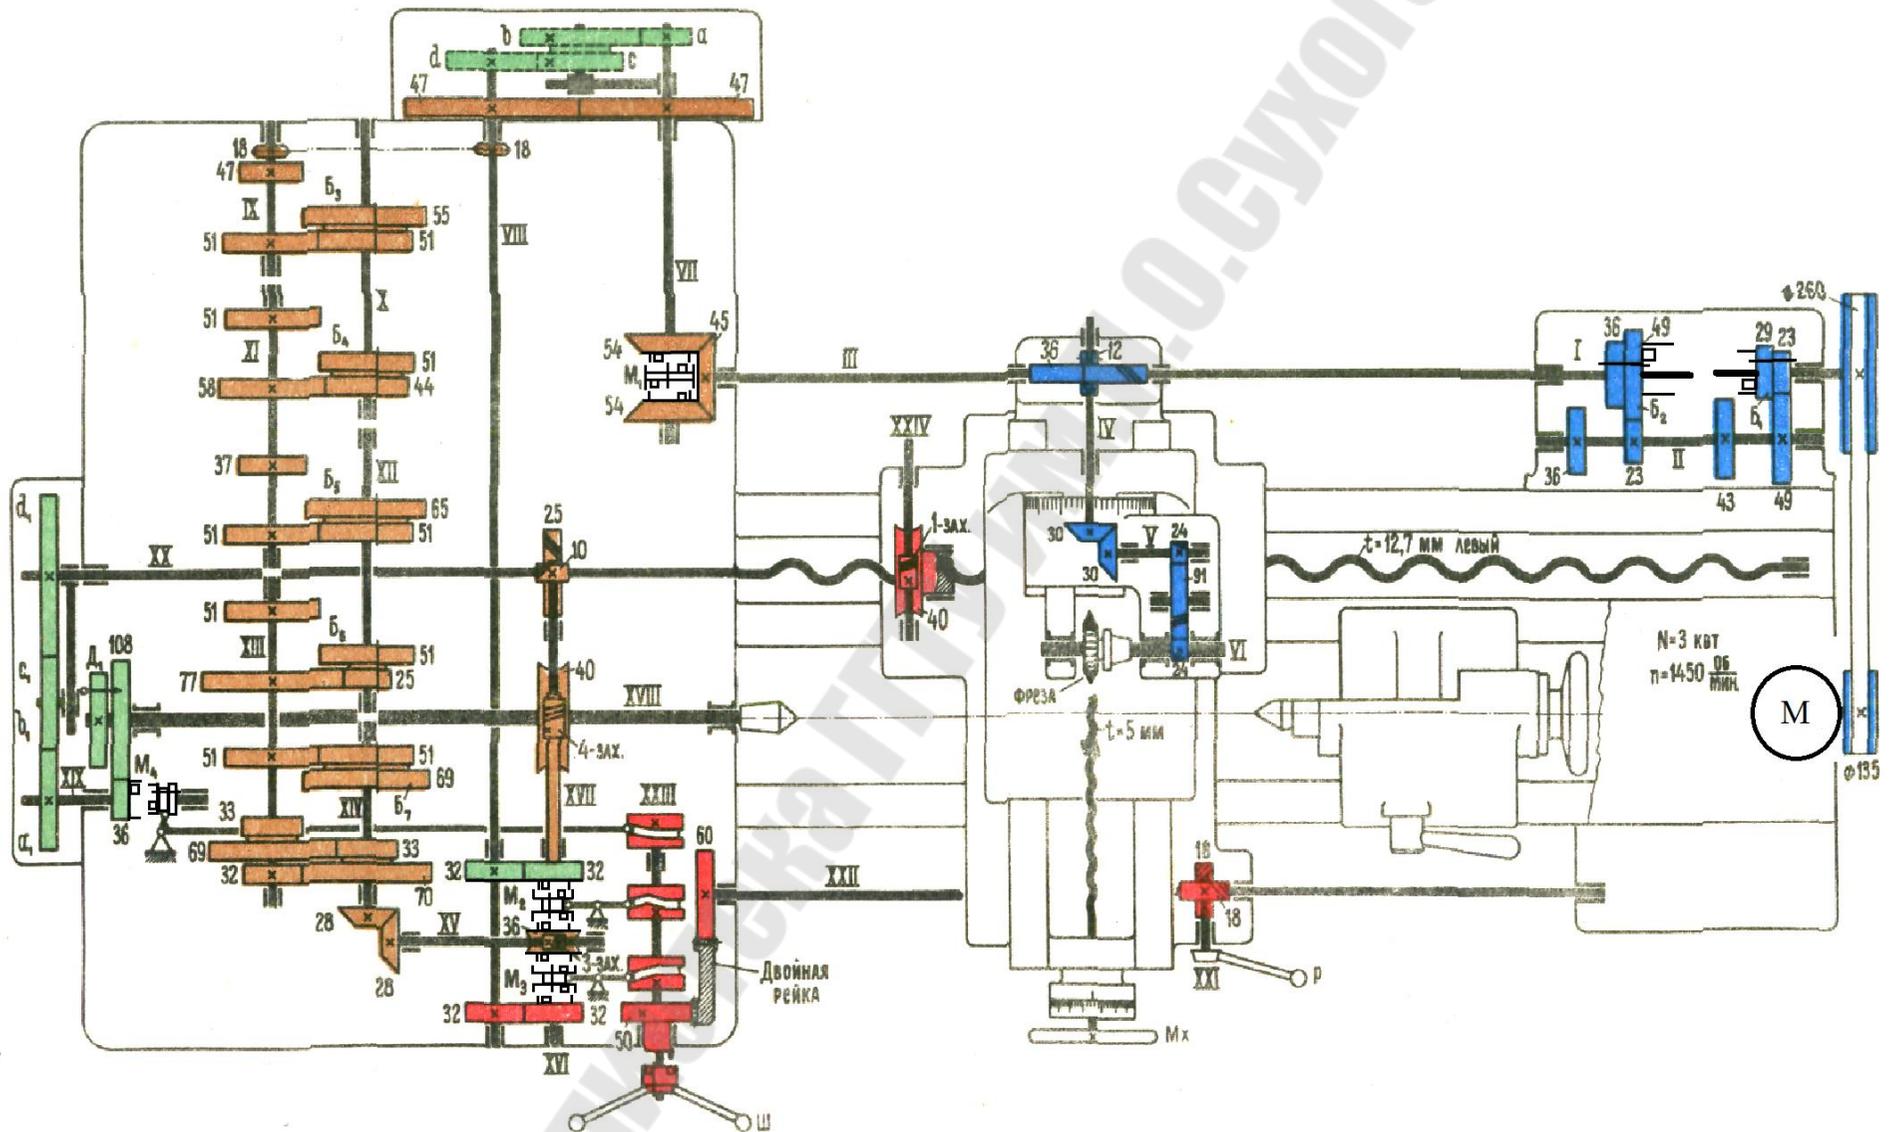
Кинематическая схема резьбофрезерного станка
